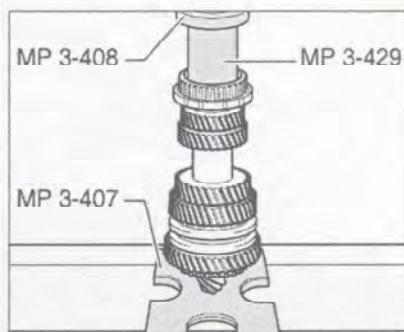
Установка ступицы синхронизатора 5-й передачи/передачи заднего хода.
